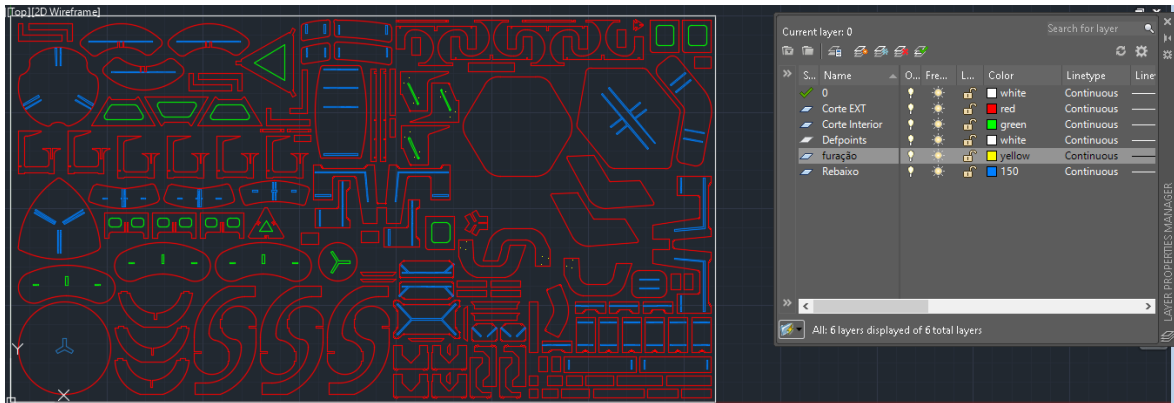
Preparação do ficheiro para corte em AutoCAD
